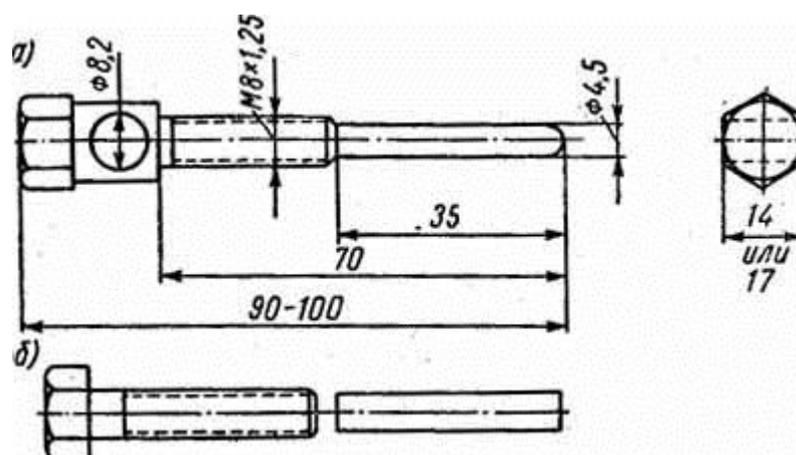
Приспособления для снятия ротора генератора: а - съемник; б - болт и штырь
